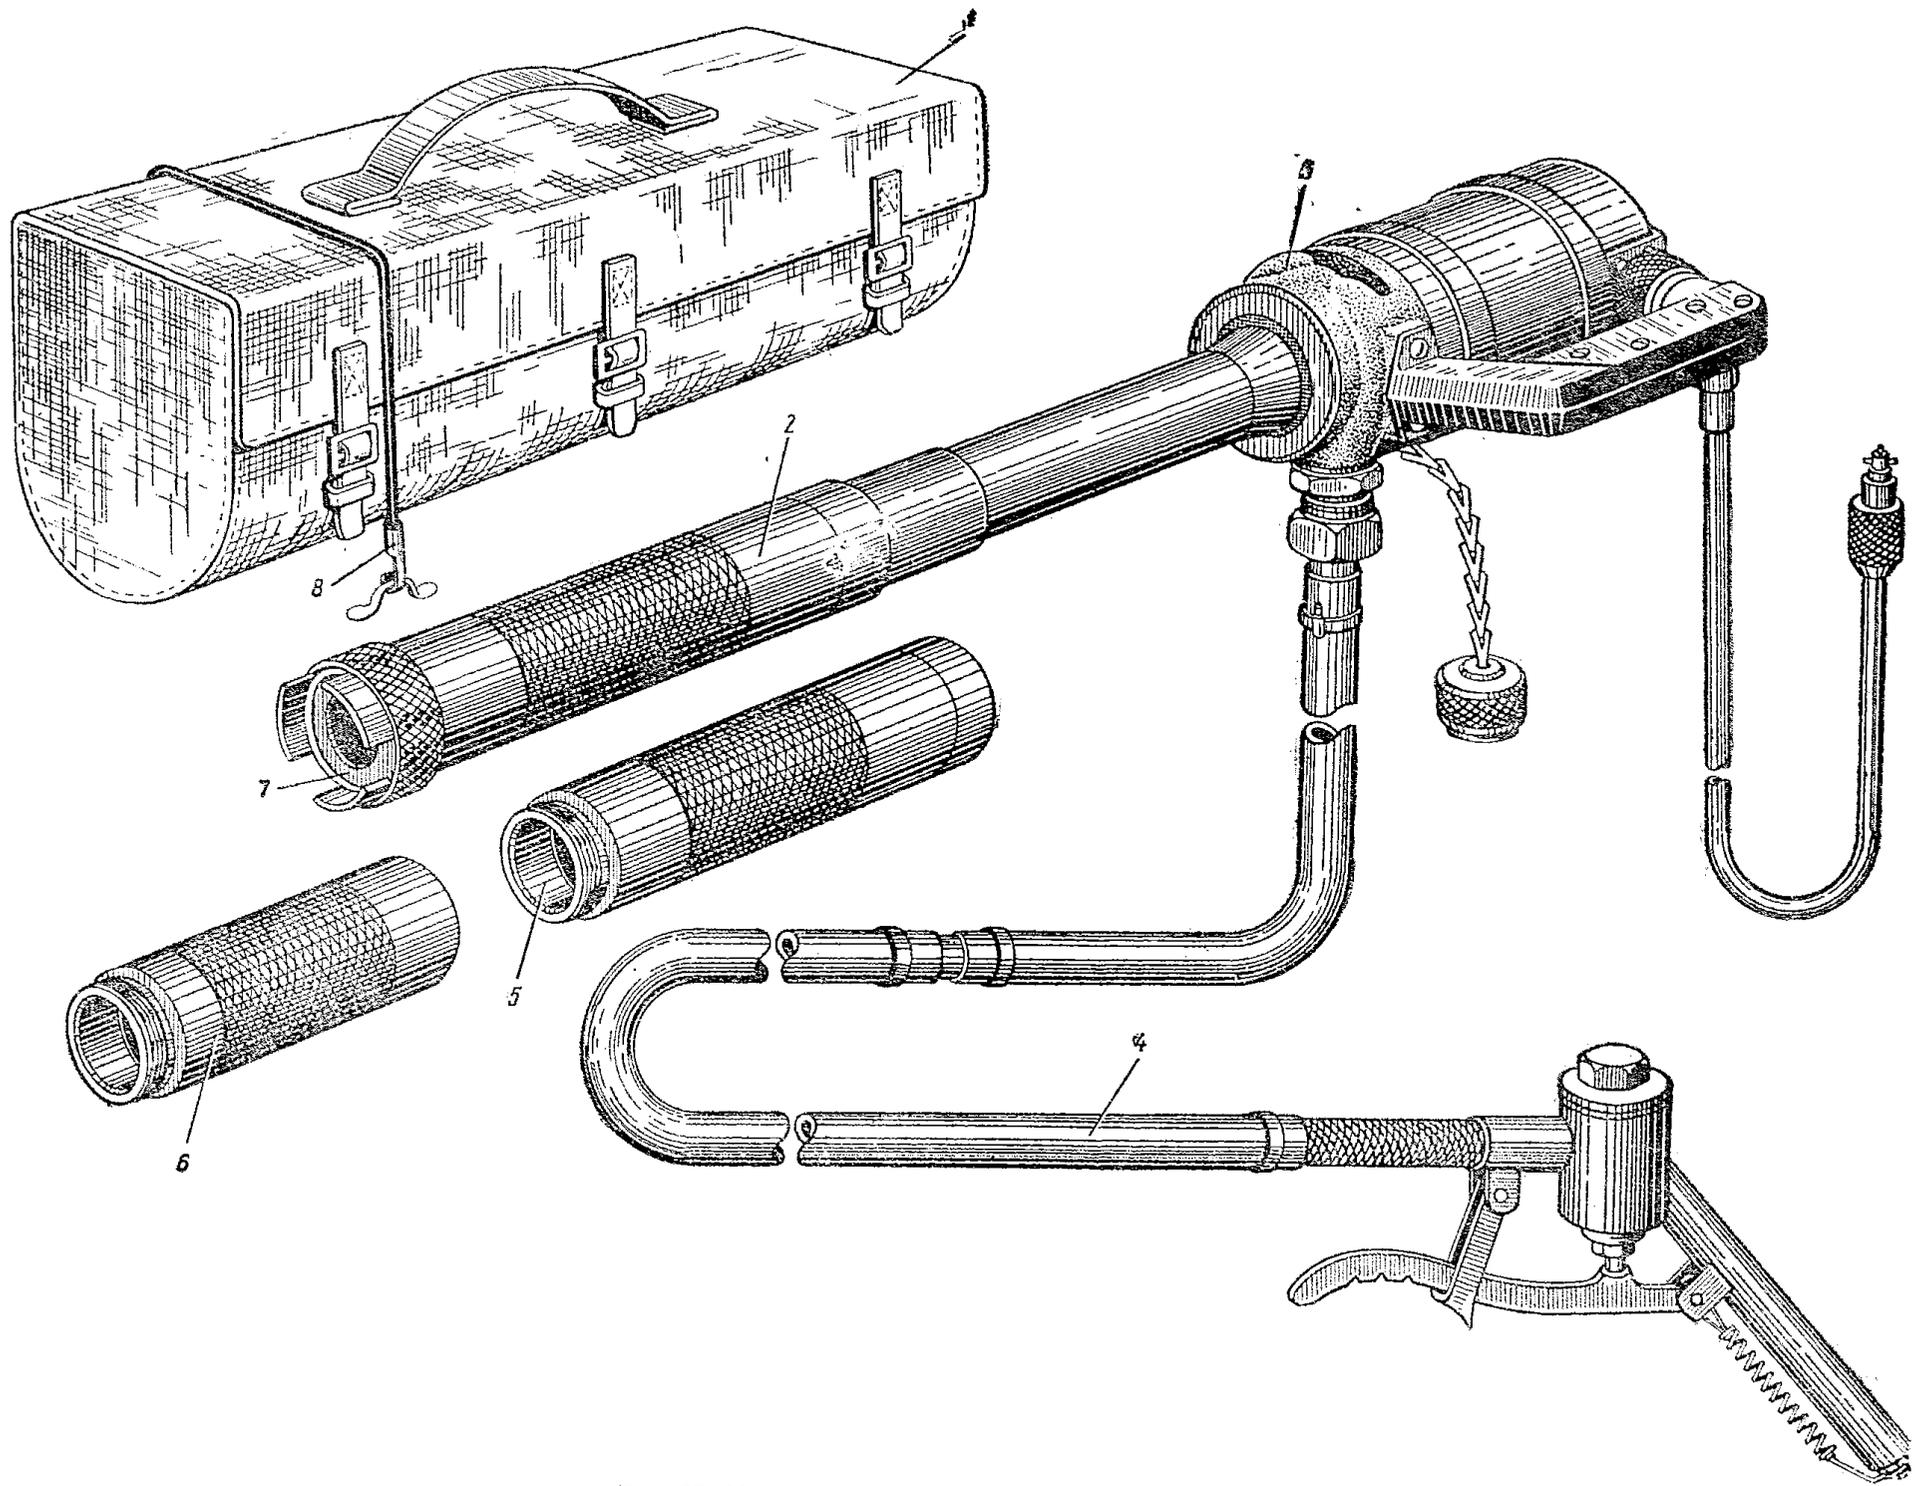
Малогабаритный заправочный агрегат МЗА-3
